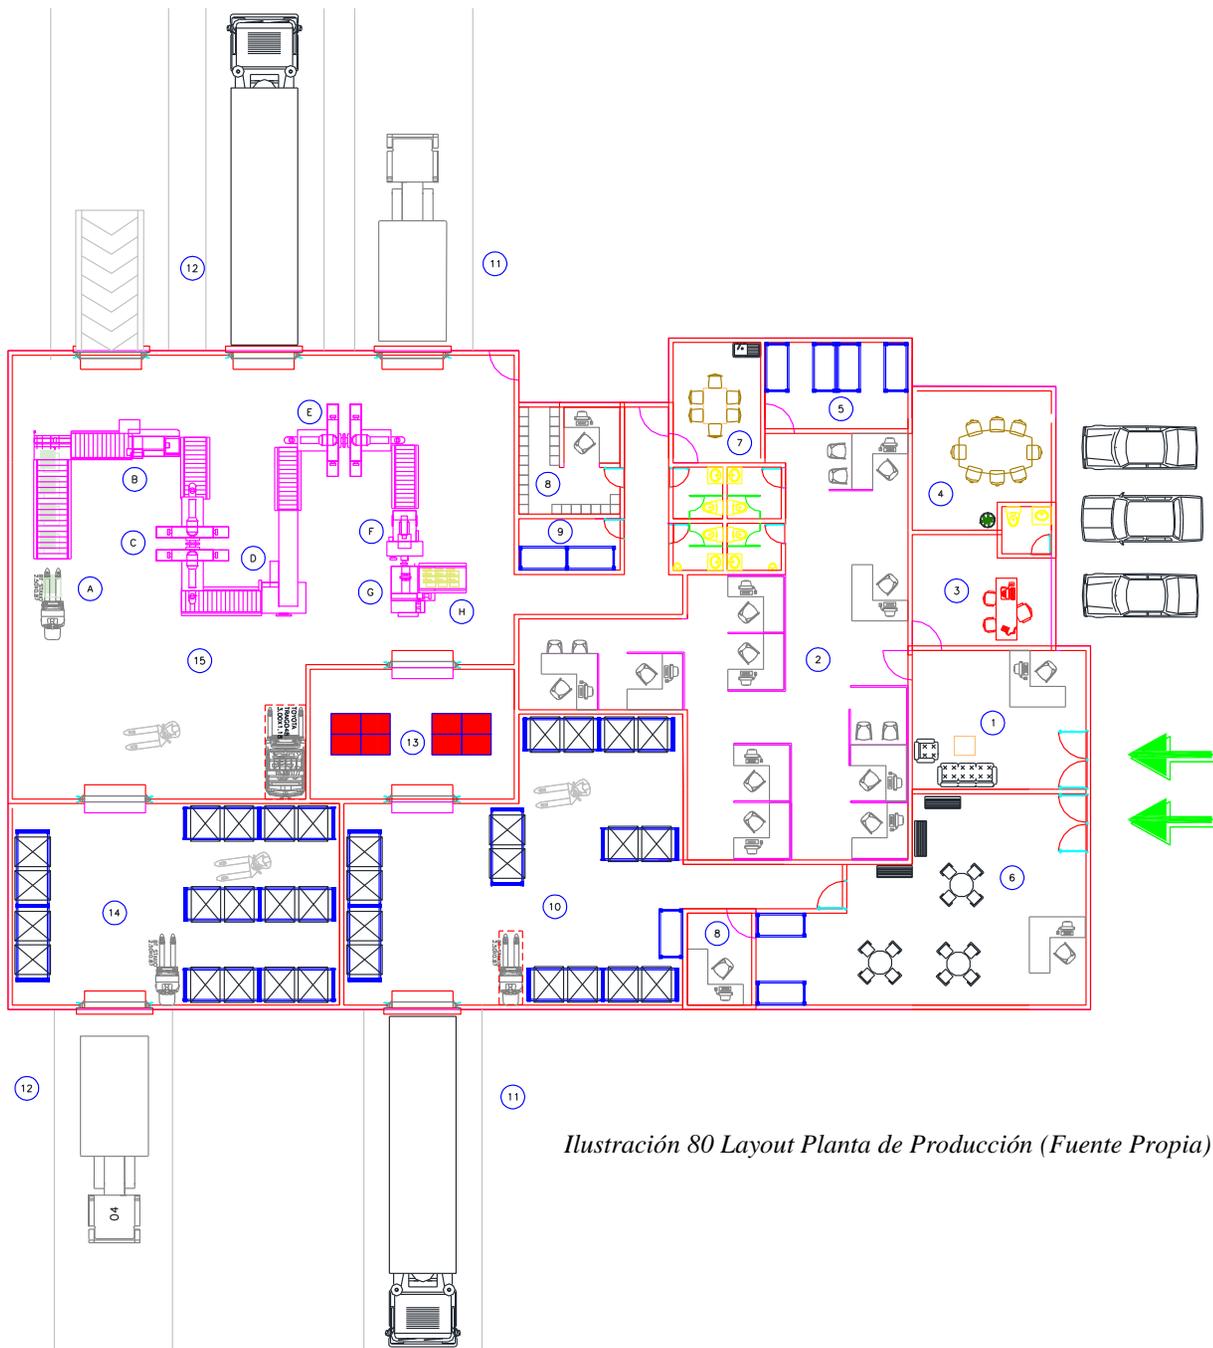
Layout Planta de Producción (Fuente Propia)
